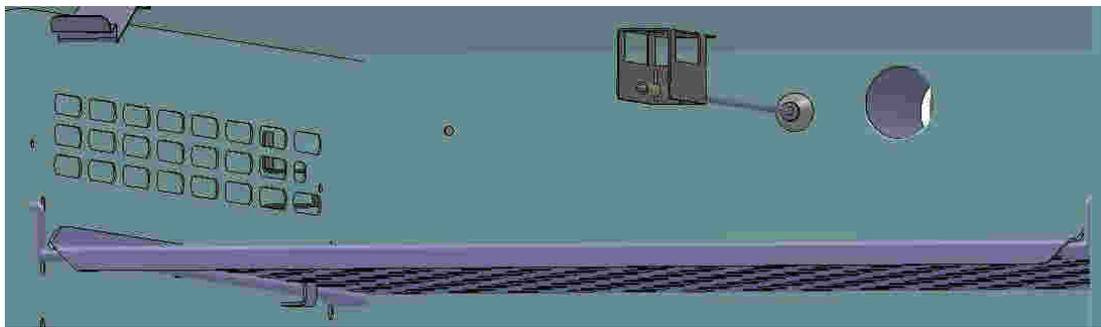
Localizzazione del sensore – serie OMH - apparecchi da pavimento
